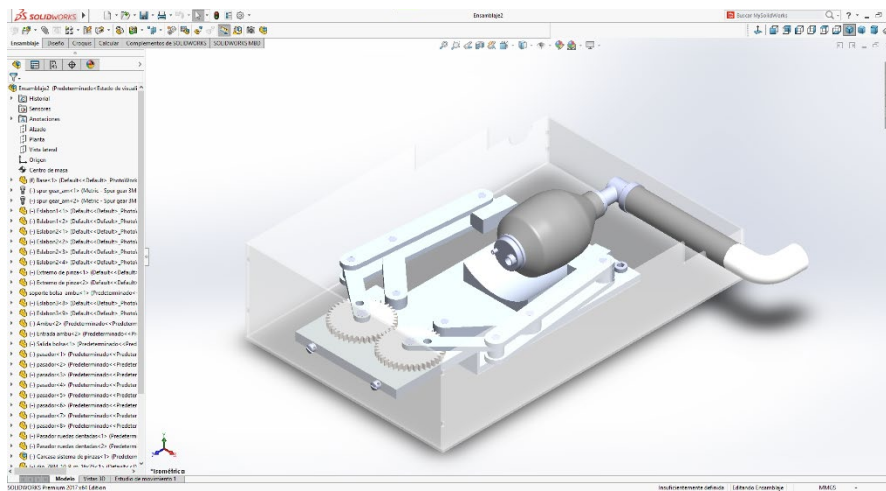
Ensamblaje estructurado en el software de diseño CAD
